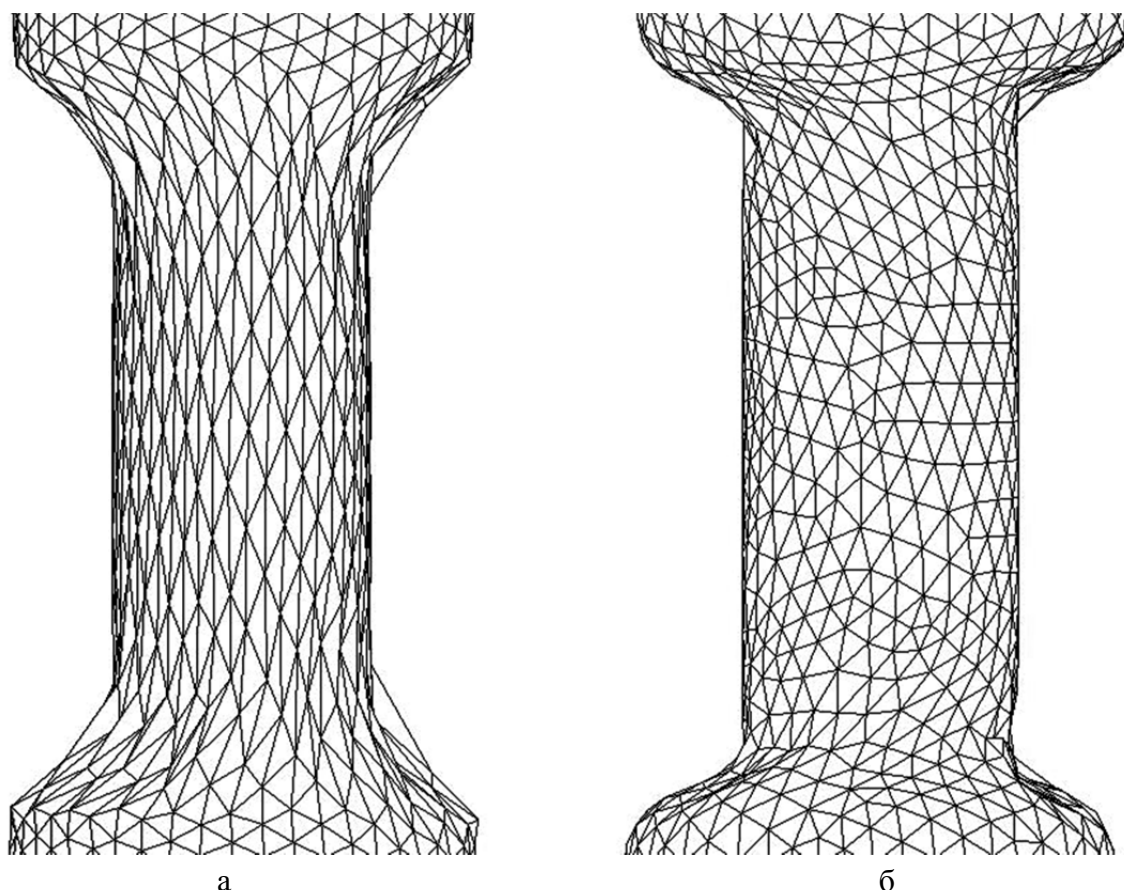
Конечно-элементная сетка заготовки на этапе калибрования:
